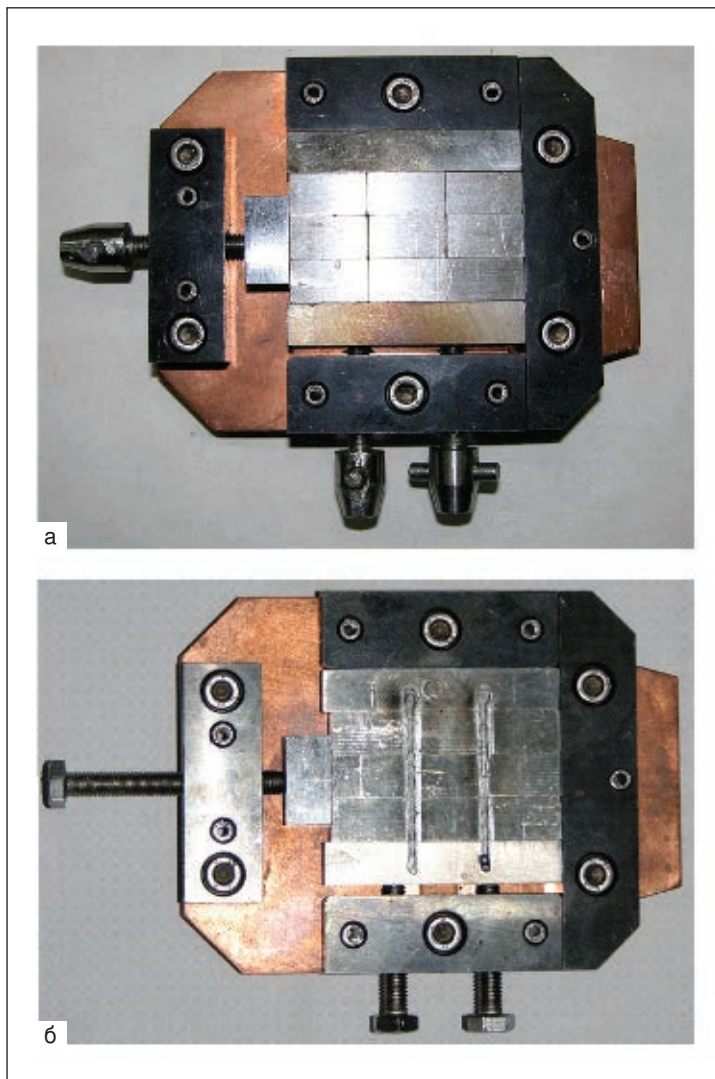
Кондуктор с заготовкой до сварки (а) и после сварки (б)
